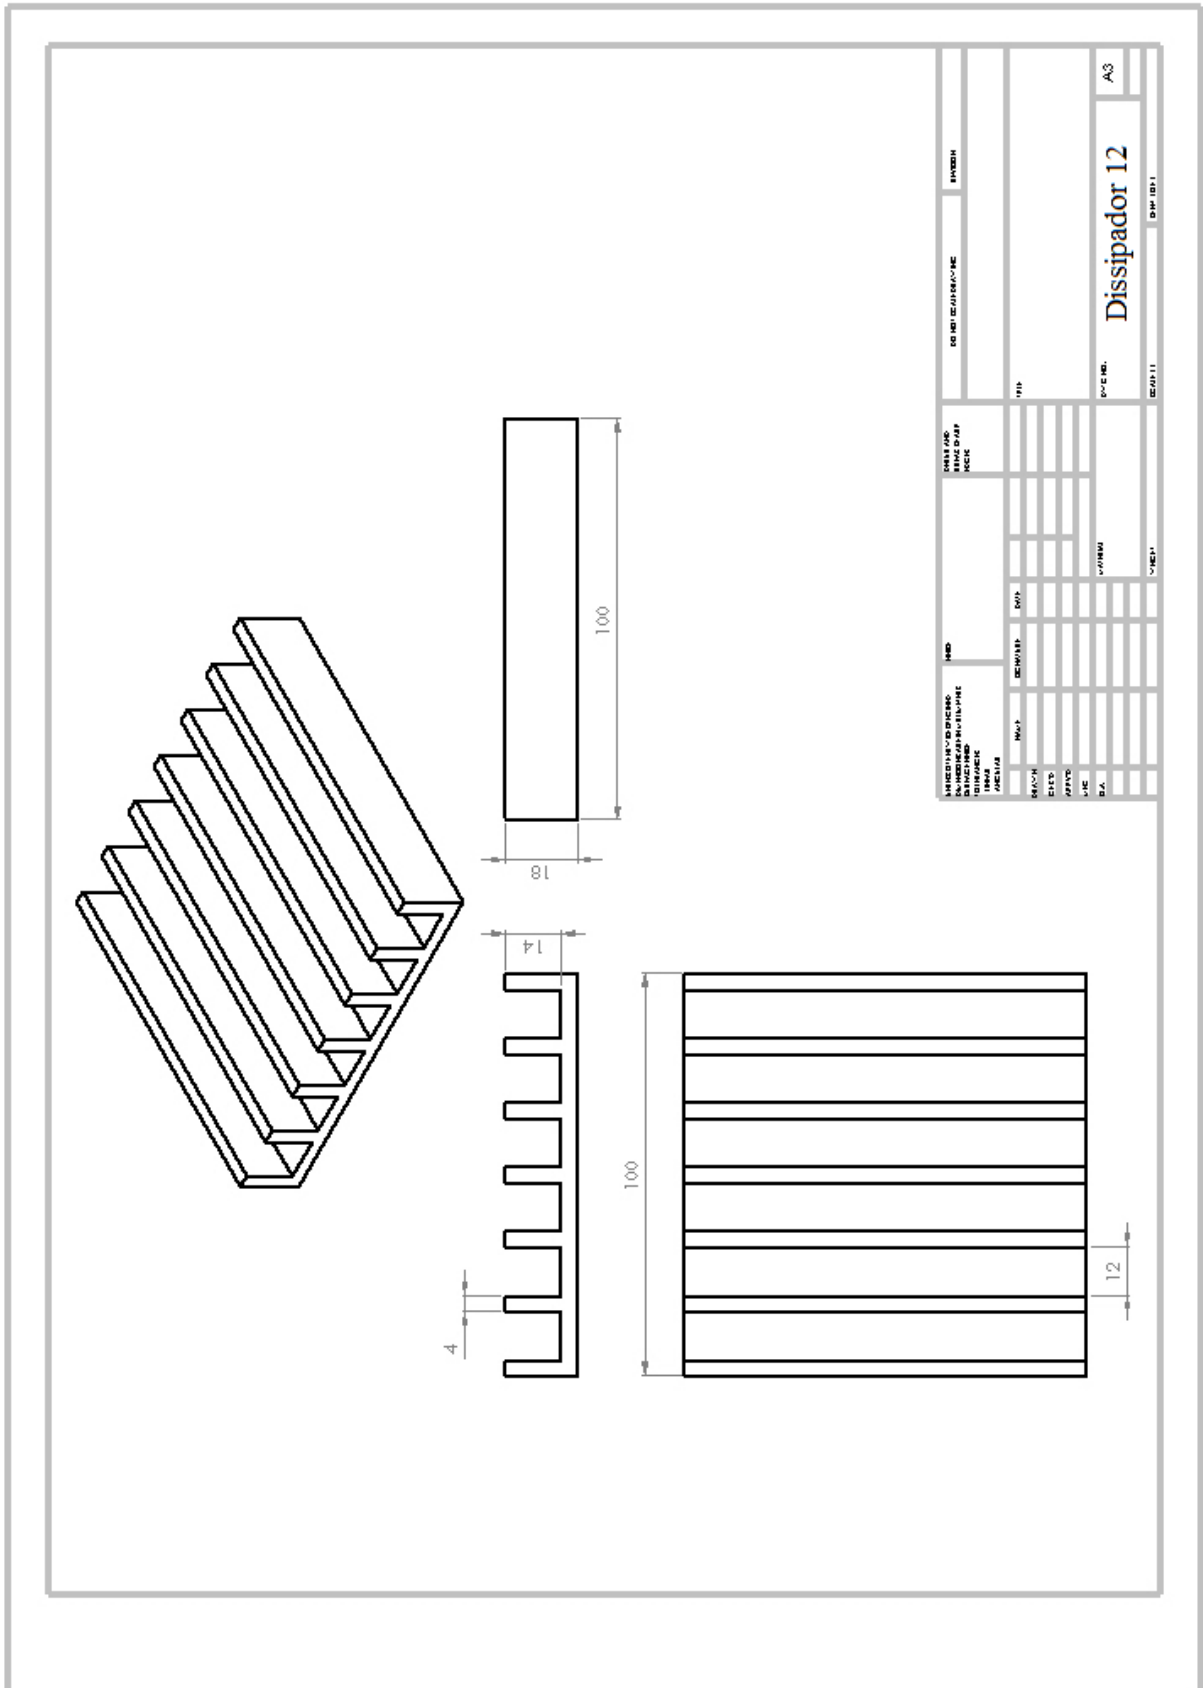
Desenho técnico utilizado para confecção do Dissipador 12.
